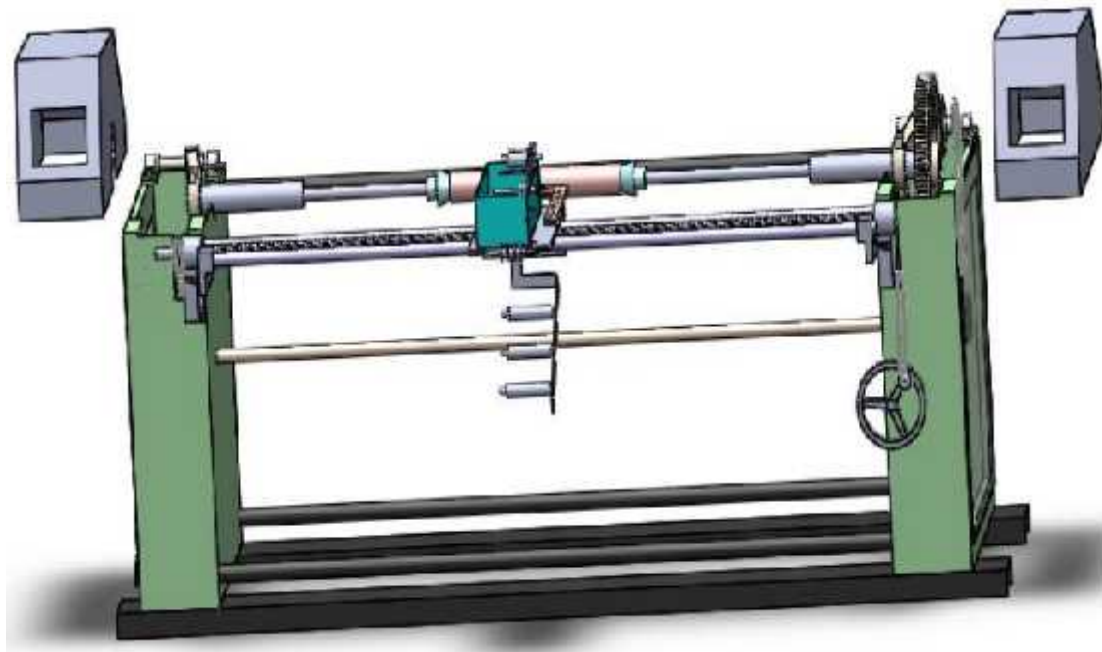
Assemblage de la machine avec « solidworks ». [18]
